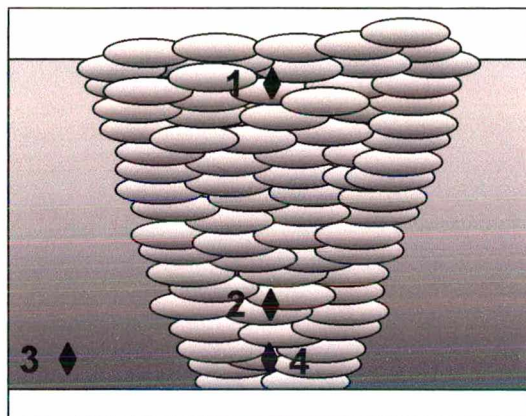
Aspecto superficial da junta soldada.
